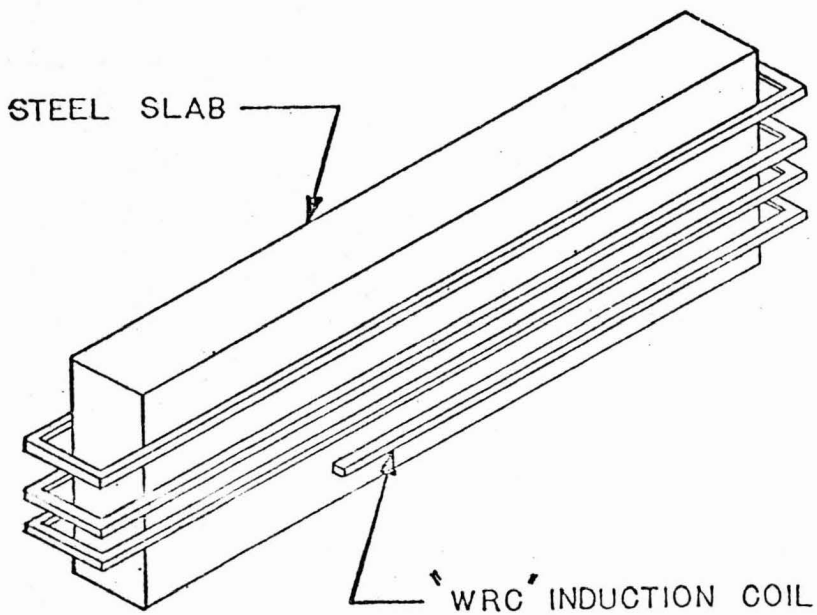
Bobina retangular larga (WRC) para aquecimento de placas.
